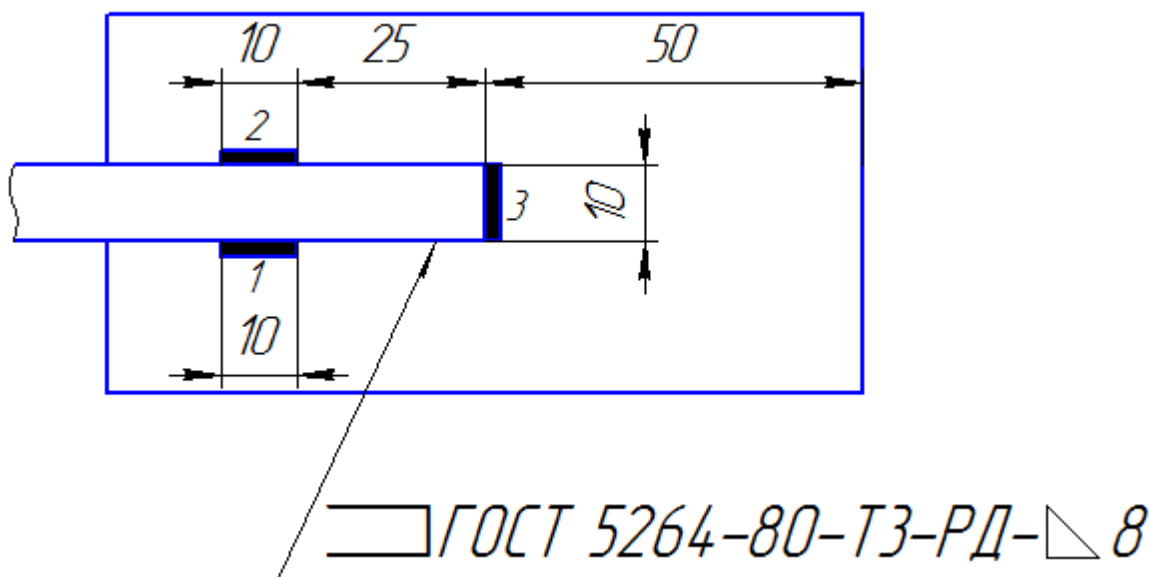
Сборка ножки стойки с упорной пластиной с помощью прихваток
